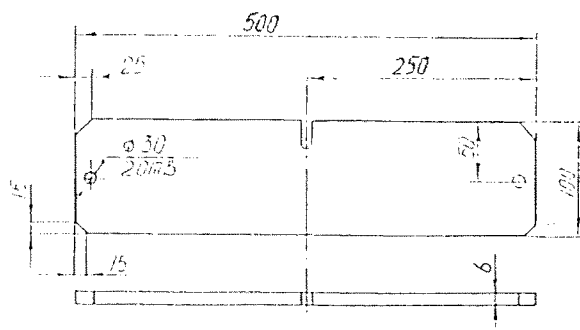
Плоский образец без наплавки сварочных швов
